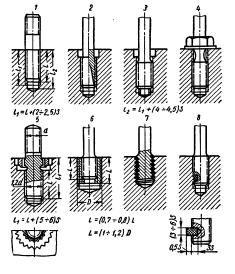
Конструктивные формы и соотношения для резьбовой части шпилек
